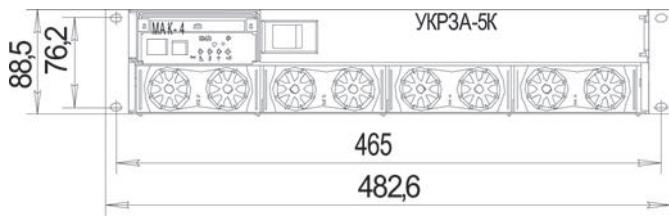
Габаритный чертеж УКРЗА-5К
